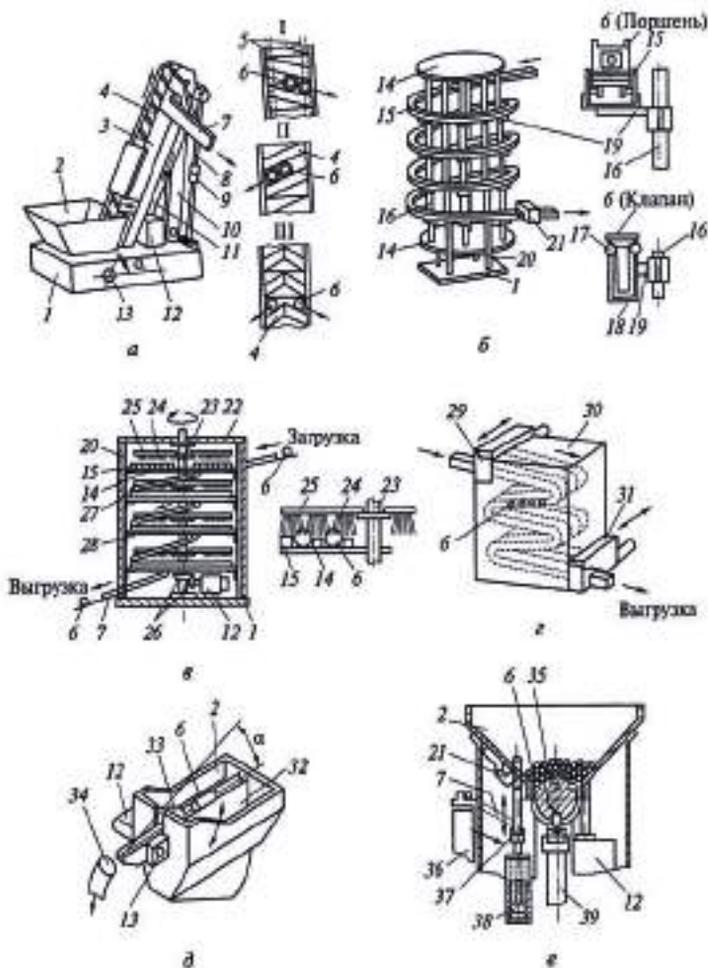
Автоматические накопители: а – бункер; б – магазин со спиральным лотком; в – ногодисковый магазин с щетками; г – лотковый магазин; д – бункер с ножевым захватом; е – магазин с барабанным захватом; 7 – основание; 2 – чаша; 3 – подъемник; 4 – планка; 5 – цепи; б – деталь; 7, 11, 75, 27 – лотки; 8 – тяга; 9 – муфта; 10 – цепная передача; 72 – редуктор; 13 – ось; 14 – диски; 16 – стяжка; 77 – проволока; 18 – скоба; 19 – кронштейн; 20 – швеллер; 21 – отсекаль; 22 – крышка; 23 – вал; 24 – щетка; 25 – щеткодержатель; 26 – зубчатые колеса; 28 – уголок; 29 – распределительный механизм; 30 – варной каркас; 31 – механизм выдачи; 32 – нож; 33 – сбрасыватель; 34 – трубка; 35 – барабан; 36, 39 – конвейеры; 37 – шибер; 38 – гидроцилиндр [17]
